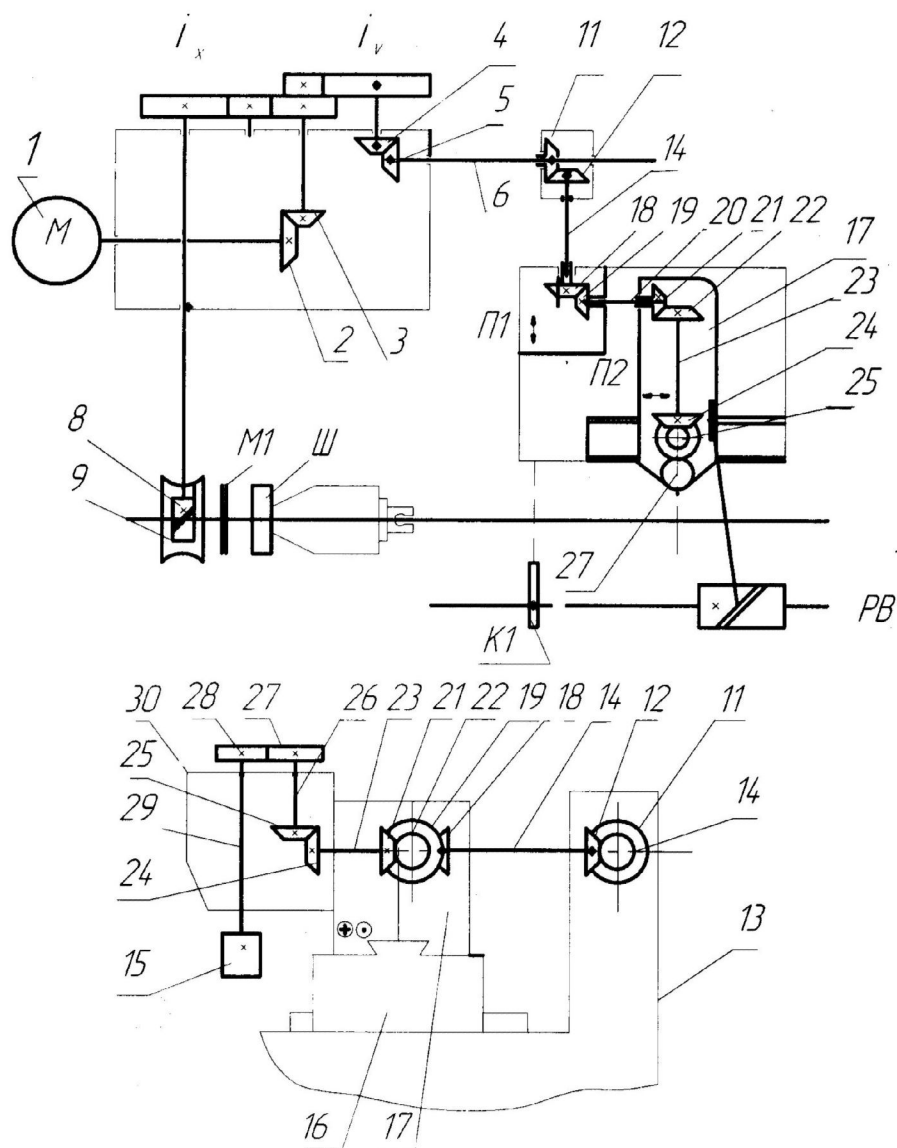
Кинематическая схема приспособления для зубофрезерования цилиндрических колес
